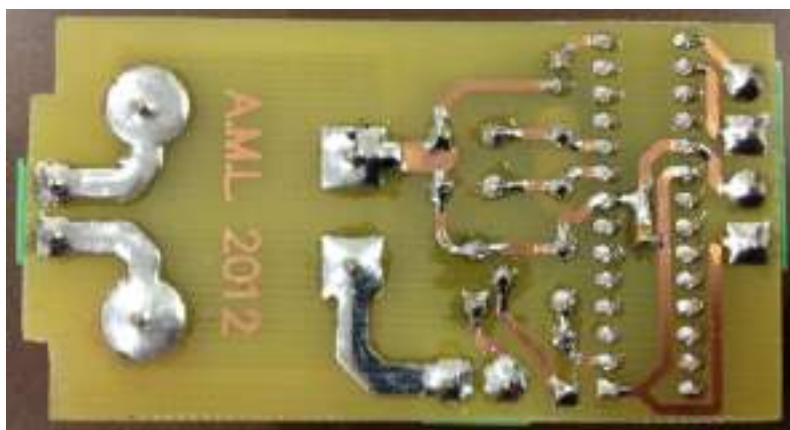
Soldaduras placa del prototipo de conductímetro para laboratorio.
